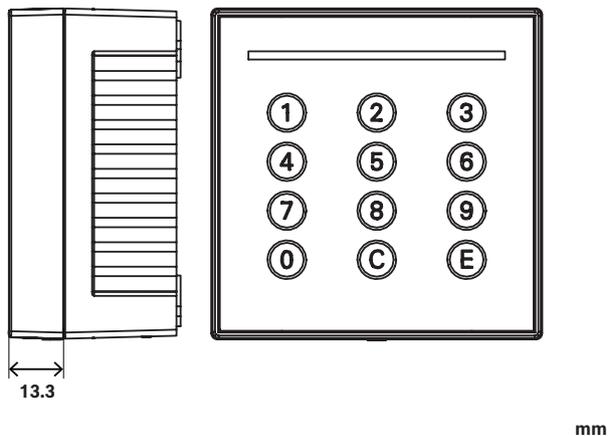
Dimensões do leitor com suporte de parede fixo e caixa de montagem
